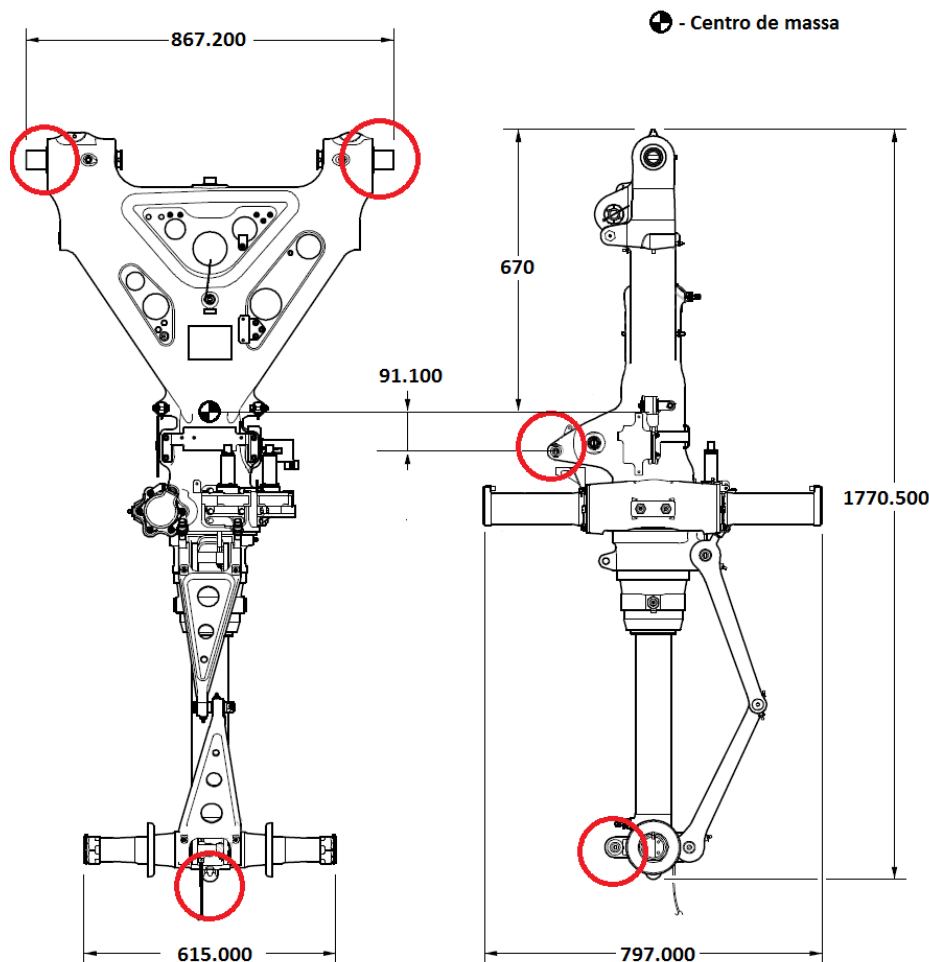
Dimensões e locais de apoio do trem de pouso. [Fonte: o autor].
